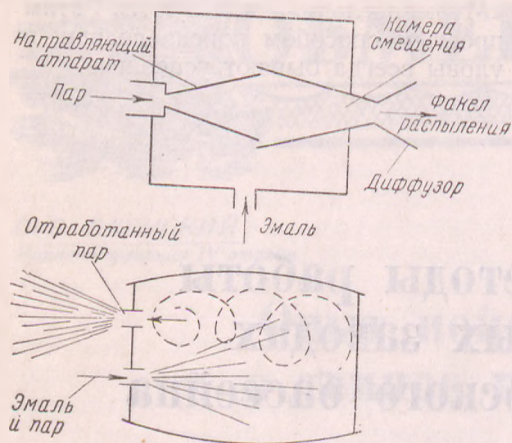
Схема устройства и принципы действия пароструйного аппарата.
